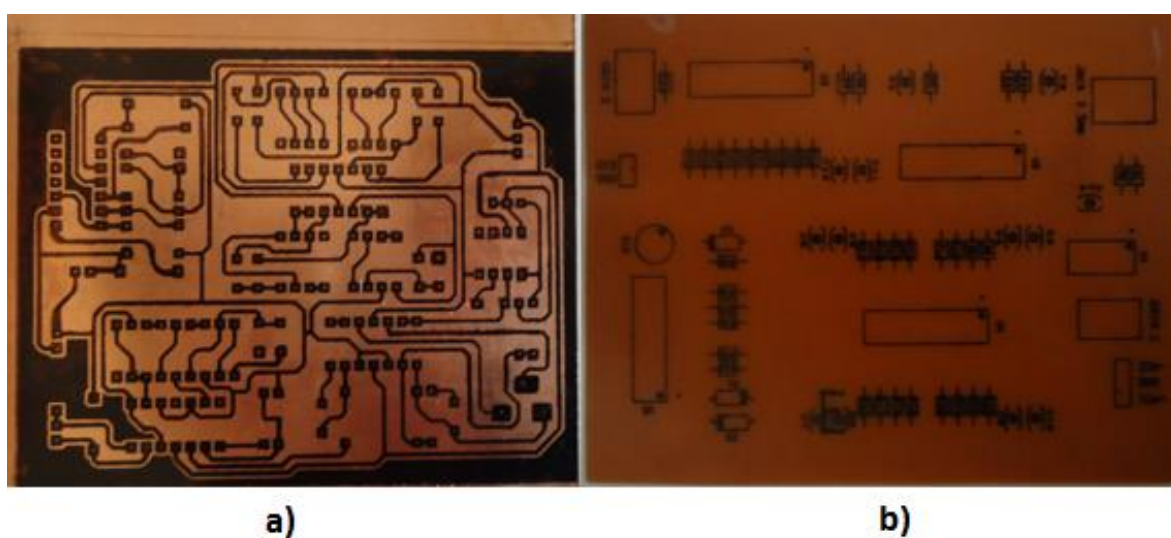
Impresión de circuito y máscara de componentes en la placa de cobre.
